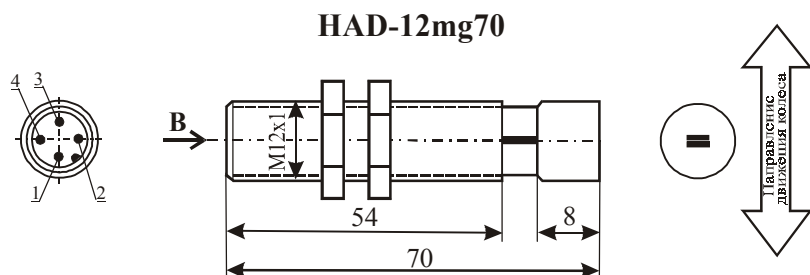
Внешний вид и габаритные размеры датчиков типа HAD-12mg70
